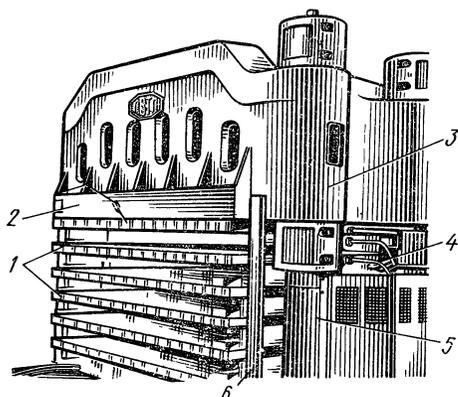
Гидравлический этажерочный пресс: 1 — передвижные прессующие плиты с паровым обогревом, 2 — верхняя траверса, 3 — упоры для плит, 4 — паропровод, 5 — колонны пресса, 6 — стойка
